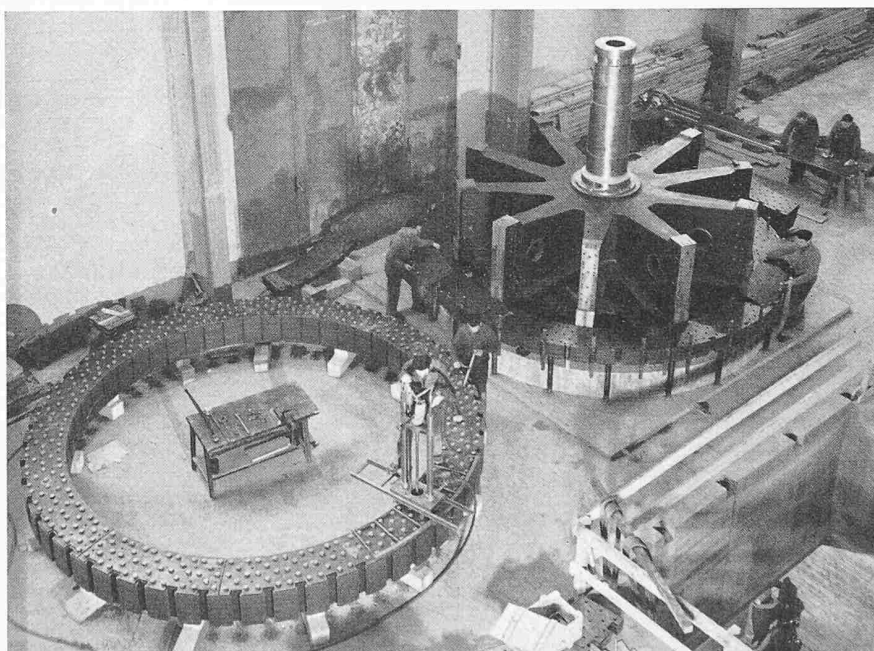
Montage des Generator-Polrades im Maschinenhaus. Rechts Schichten der Blechkette eines Polradkranzes, links Ausreiben der Löcher für die Passschrauben. 4. Januar 1952
